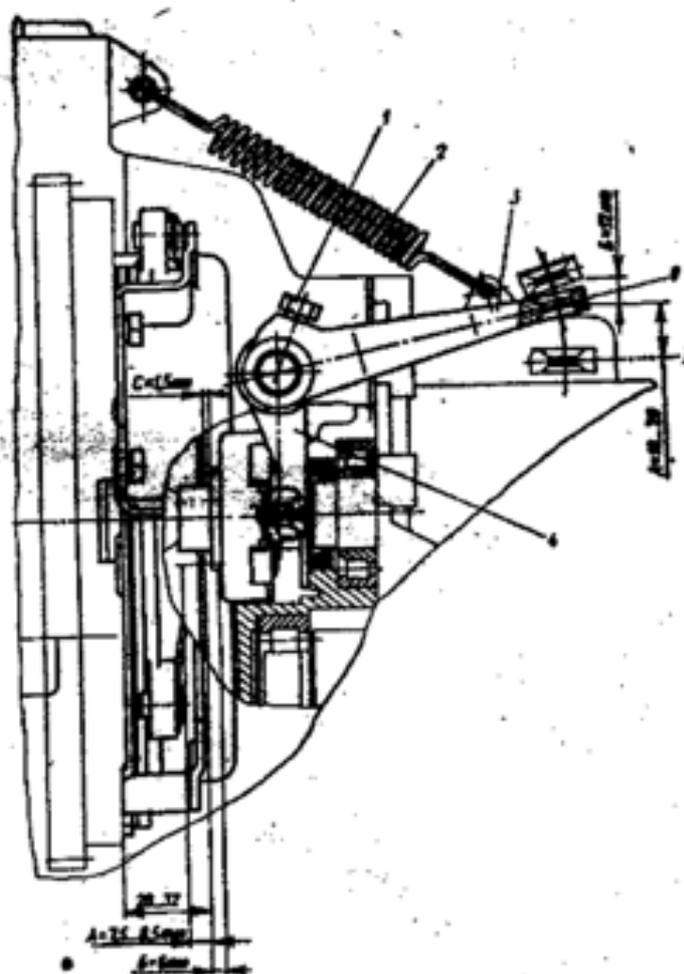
Установка сцепления: 1 - болт стопорный; 2 - пружина возвратная вилки выключения сцепления; 3 - рычаг оси вилки выключения сцепления; 4 - вилка выключения сцепления; А - ход выключения; Б - ход износа; С - свободный ход выжимного подшипника
